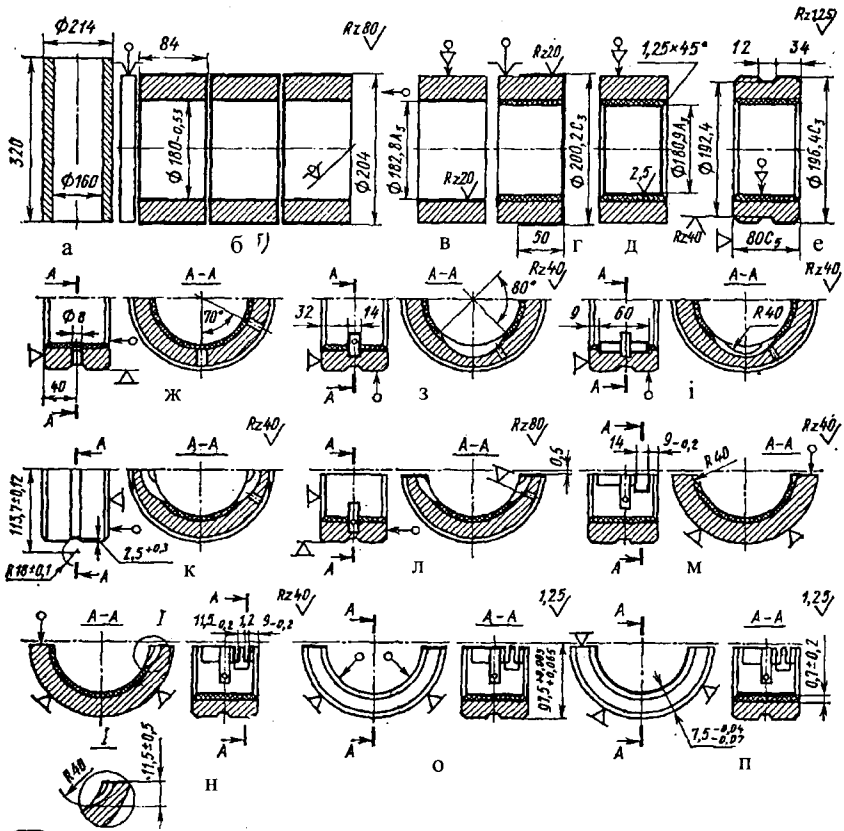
Технологічна схема механічної обробки вкладиша шатуну опозитного компресора бази М10.
